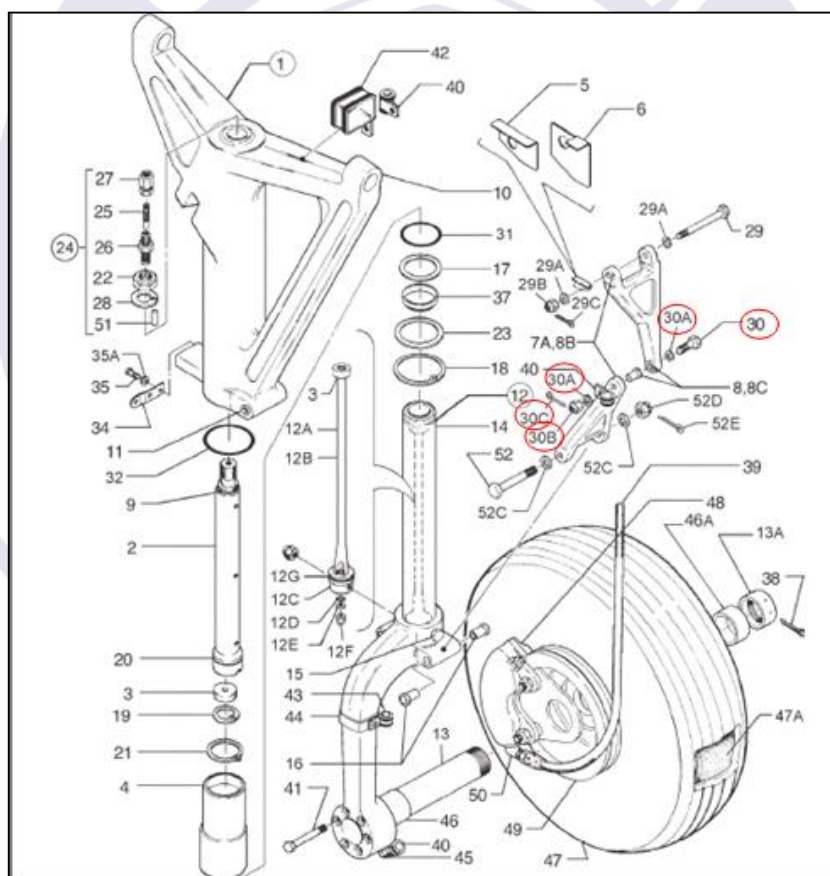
Ilustração técnica da perna do trem de pouso principal, com destaque para os componentes ausentes.
